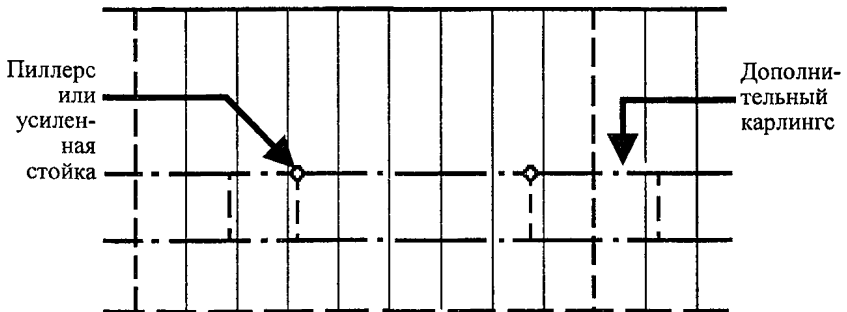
Вариант подкрепления палубного перекрытия дополнительным рамным карлингсом и пиллерсами.
